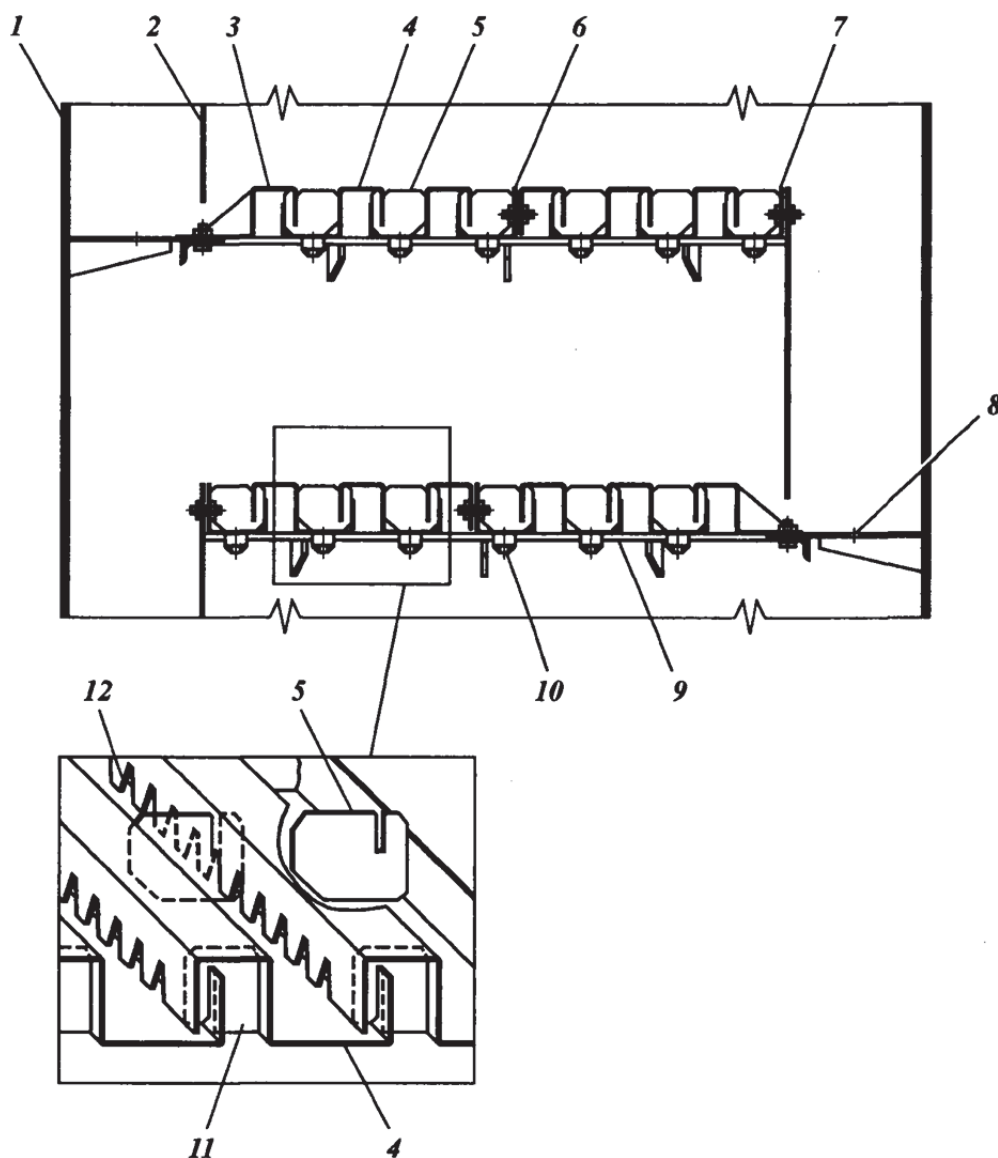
Конструкция тарелки из S-образных элементов: 1 – корпус колонны; 2 – сливная перегородка; 3 – паровой элемент; 4 – S-образный элемент; 5 – поперечные перегородки; 6 – съемный S-образный элемент; 7 – жидкостный элемент; 8 – отверстие для слива жидкости; 9 – опорное кольцо; 10 – трубочина; 11 – заглушки; 12 – прорези в S-образных элементах
